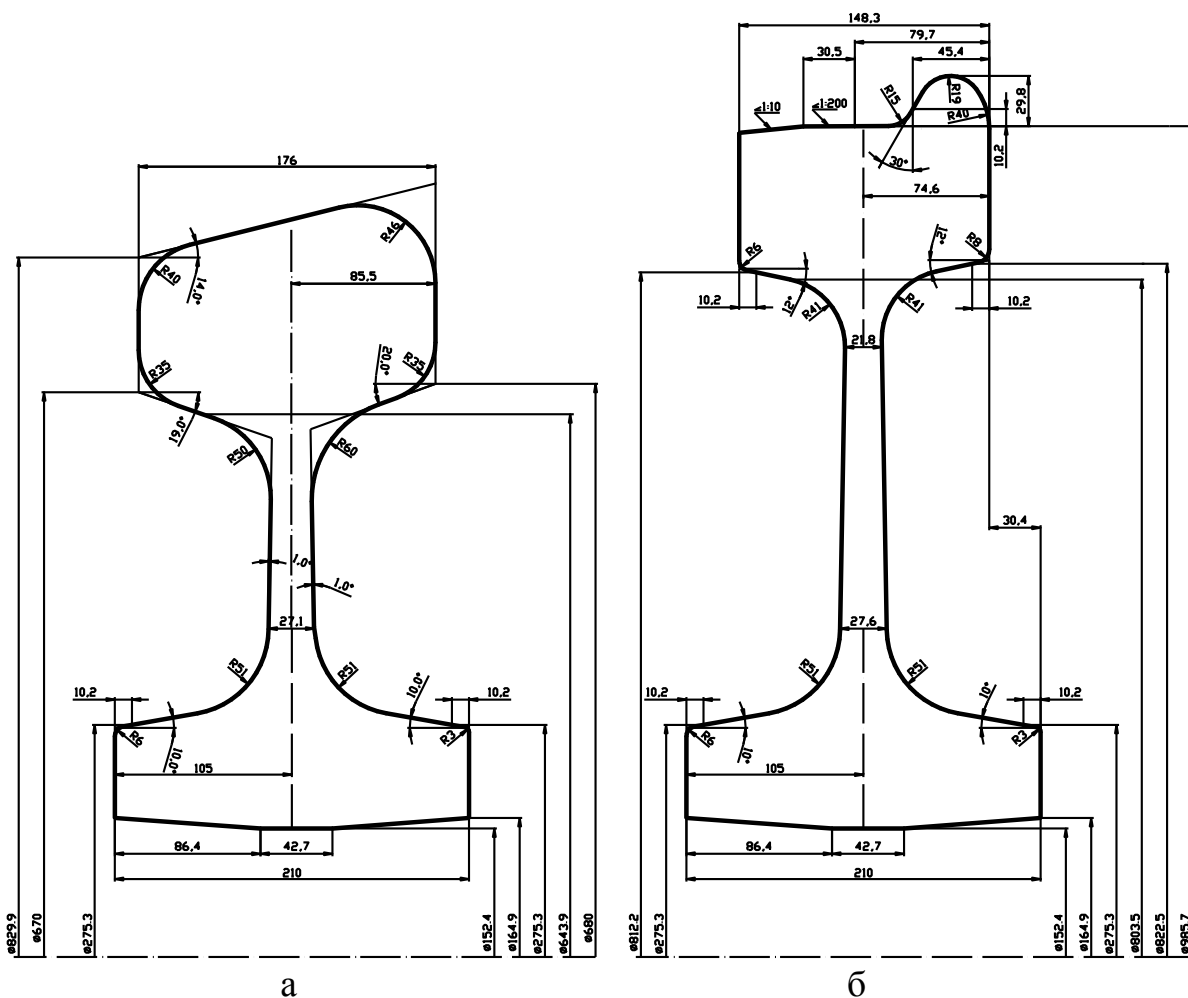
Колесная заготовка (а) и прокатываемое из него черновое колесо (б) (существующая калибровка по металлу)
